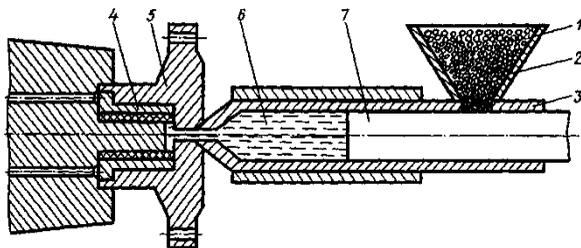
Схема восстановления деталей литьем под давлением:
